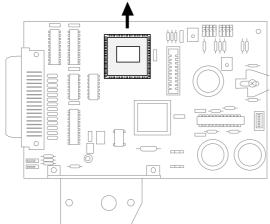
Controller auf der Leiterplatte Figure 28 Controller on the PCB
